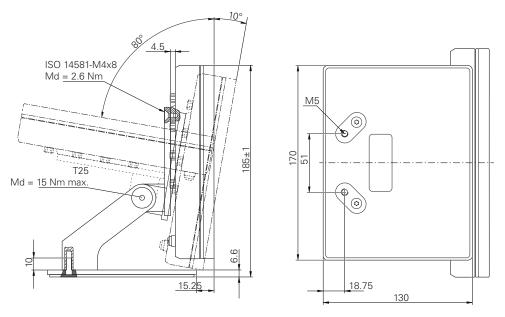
Dimensiones del aparato con pie de soporte Multi-Pos
